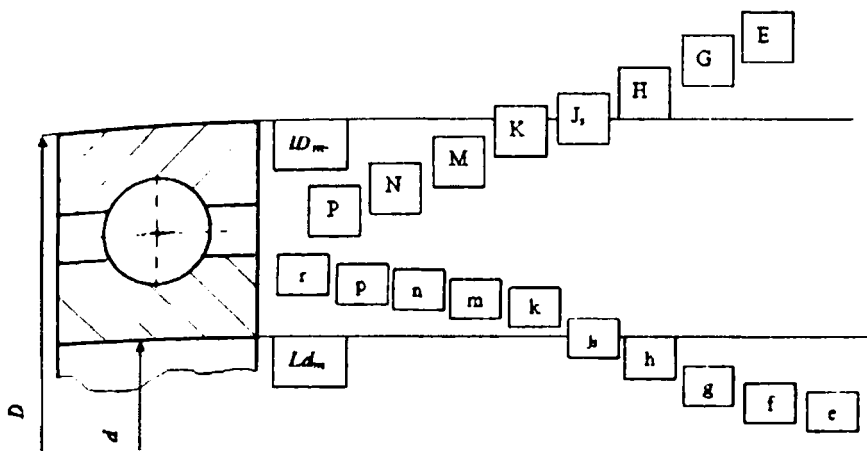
Схемы расположения полей допусков при посадках подшипников
